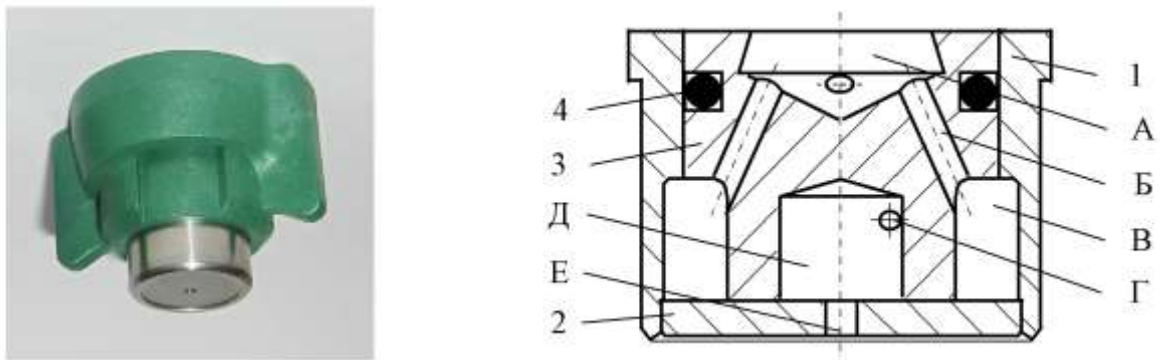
Загальний вигляд і конструктивна схема відцентрового розпилювача: 1- корпус; 2- сопло; 3- завихрювач; 4- гумове кільце.
